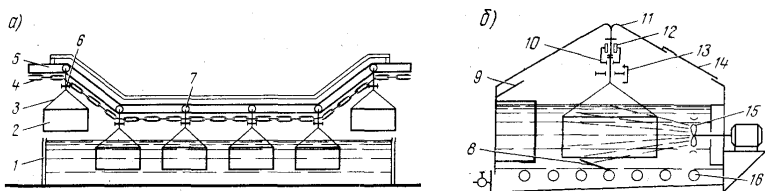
Конвеєрна мийна машина КМ-4: а – поздовжній розріз; б – поперечний розріз; 1 – ванна; 2 – контейнер; 3 – розтяжка; 4 – ланцюг; 5 – балка; 6 – шестірні; 7 – каретка; 8 – козирок; 9 – щитки; 10 – упорний підшипник; 15 – лопатевий гвинт; 16 – теплообмінник
